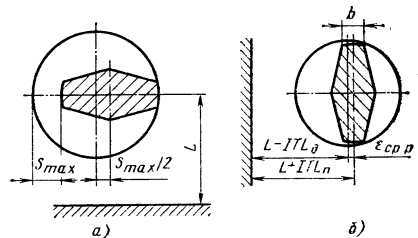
Расчетные схемы бокового зазора (а) и ширины b ленточки срезанного пальца (б) при установке заготовки цилиндрическим отверстием на срезанный палец
